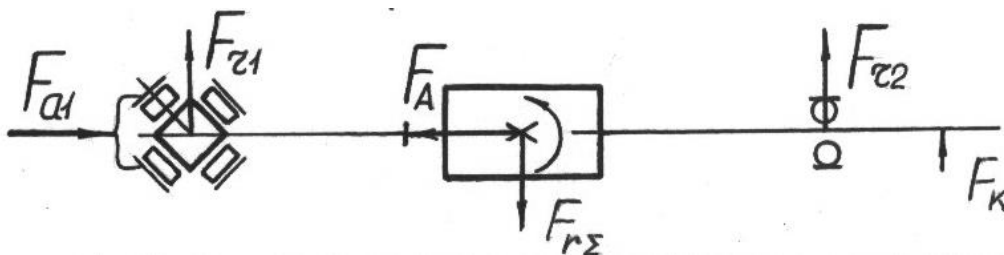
К определению ресурса конических подшипников вала червяка
